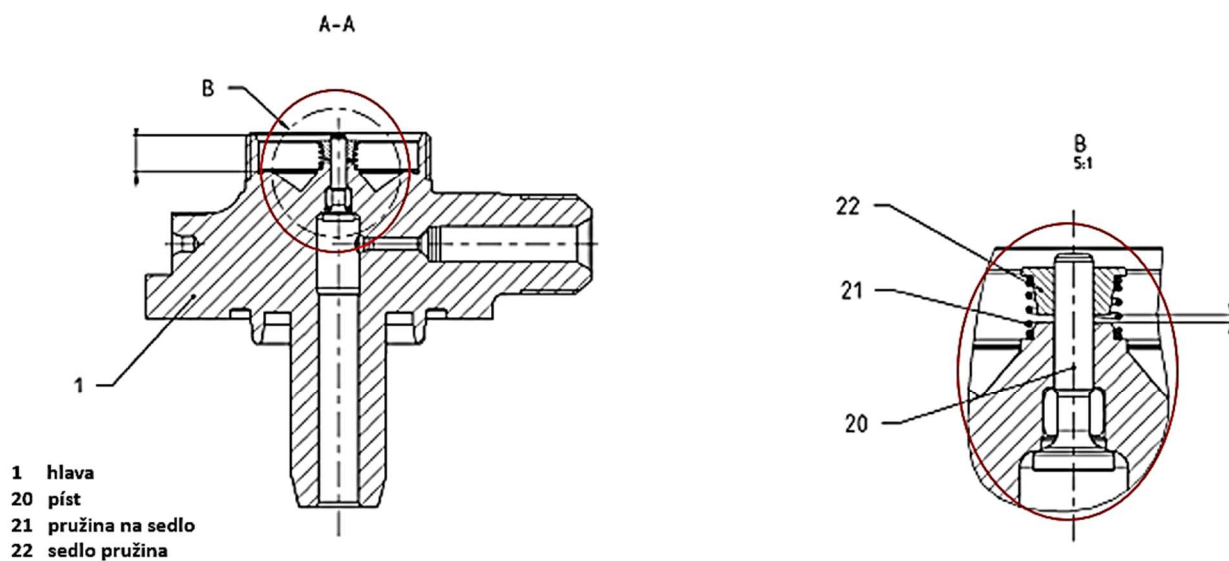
Detail standardní hlava a její funkce rozdělení tlaku [30]
